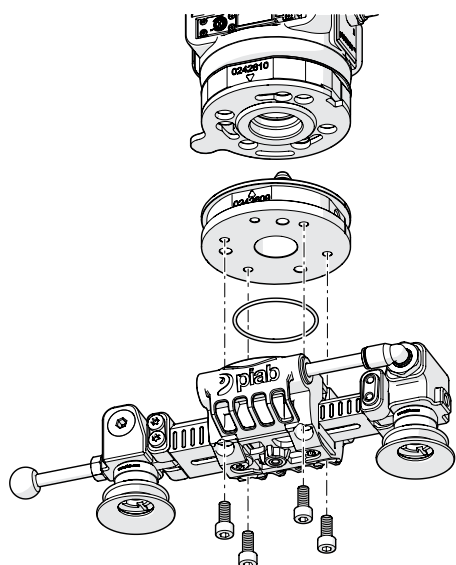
Garra ajustable montada en piCOBOT® mediante un cambiador de herramientas
